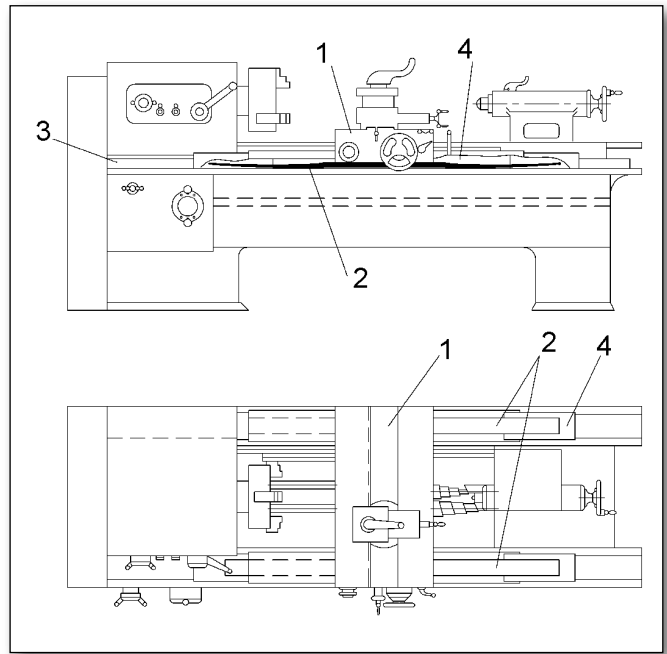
Суппорт на направляющих лыжах: 1 — суппорт; 2 — лыжи; 3 — ниша для лыжи; 4 — телескопические щетки для защиты от стружки.
